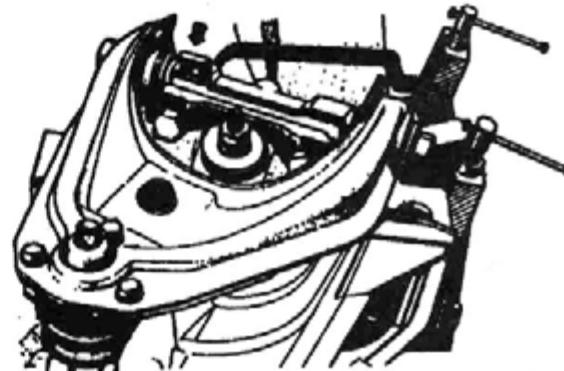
Установка скобы для регулировки продольного наклона оси поворота колес
